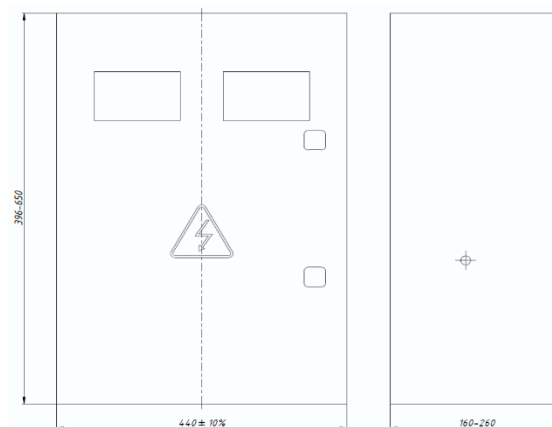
Общий вид и габаритные размеры шкафов с двумя счётчиками в пластиковом корпусе.
